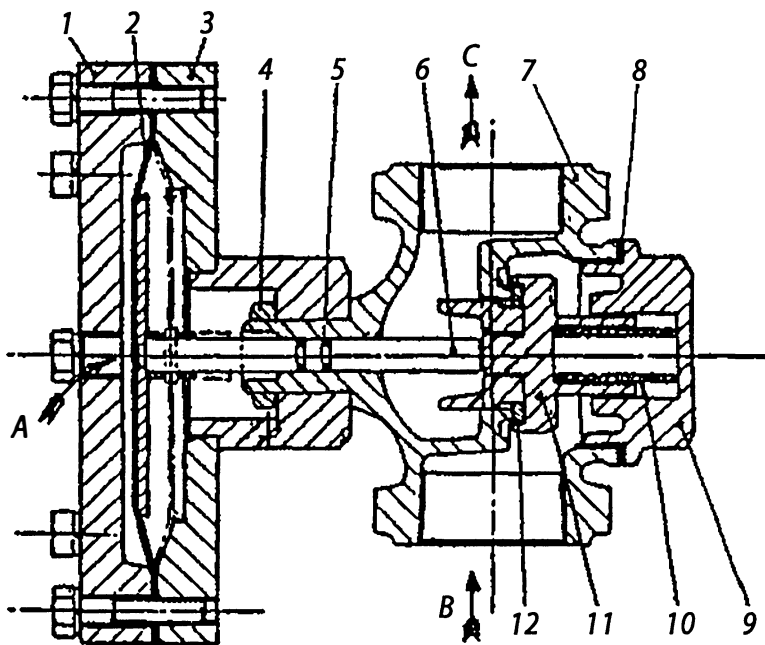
Отсечной водяной клапан: 1 — крышка; 2 — диафрагма; 3 — фланец; 4 — гайка; 5 — уплотнительное кольцо; 6 — шток; 7 — корпус клапана; 8 — прокладка; 9 — колпак; 10 — пружина; 11 — клапан; 12 — рабочая кольцевая пластина; А — вход воздуха под мембрану охладителя первой ступени; В — вход охлаждающей воды от насоса; С — вход воды в компрессор
